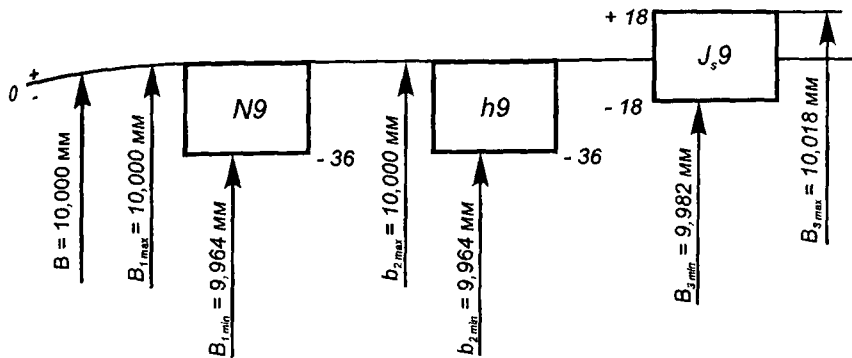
Схема расположения полей допусков шпоночного соединения
